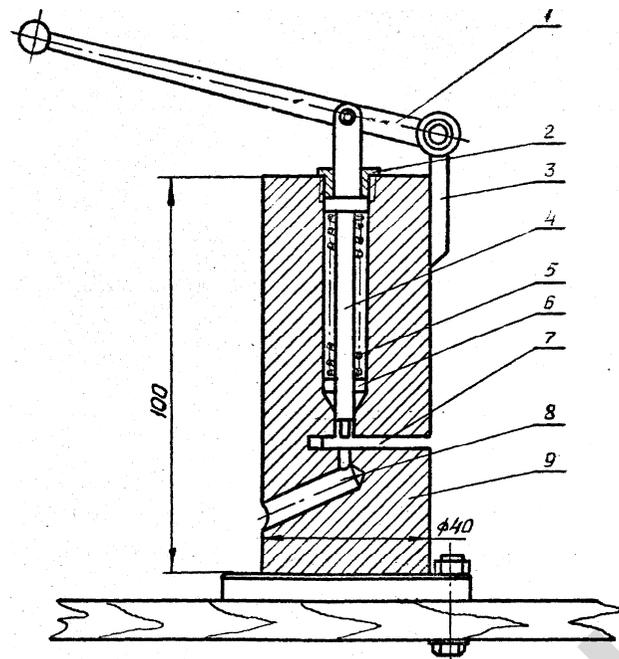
Приспособление для прошивки отверстий в мембранах:
